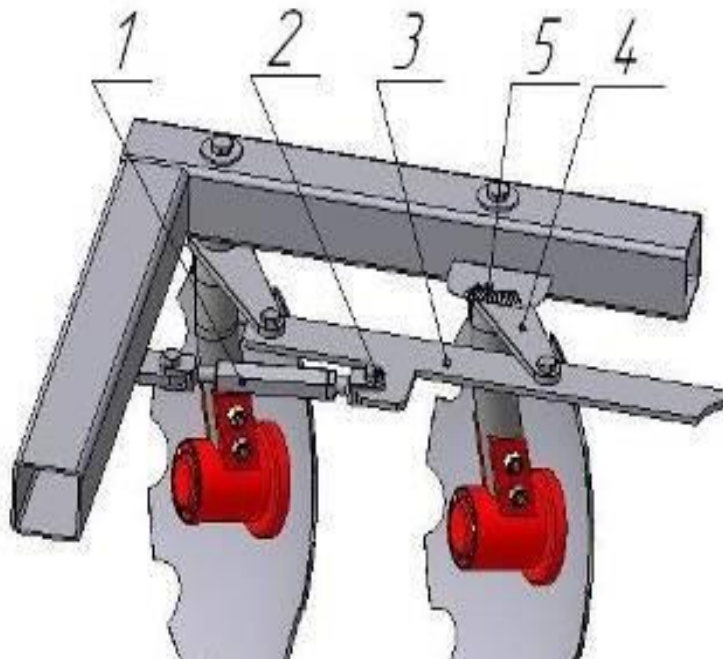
Механизм регулировки угла атаки: 1 – талрепный вилочный наконечник; 2 – гайка; 3 – планка; 4 – указатель угла атаки; 5 – шкала угла атаки
